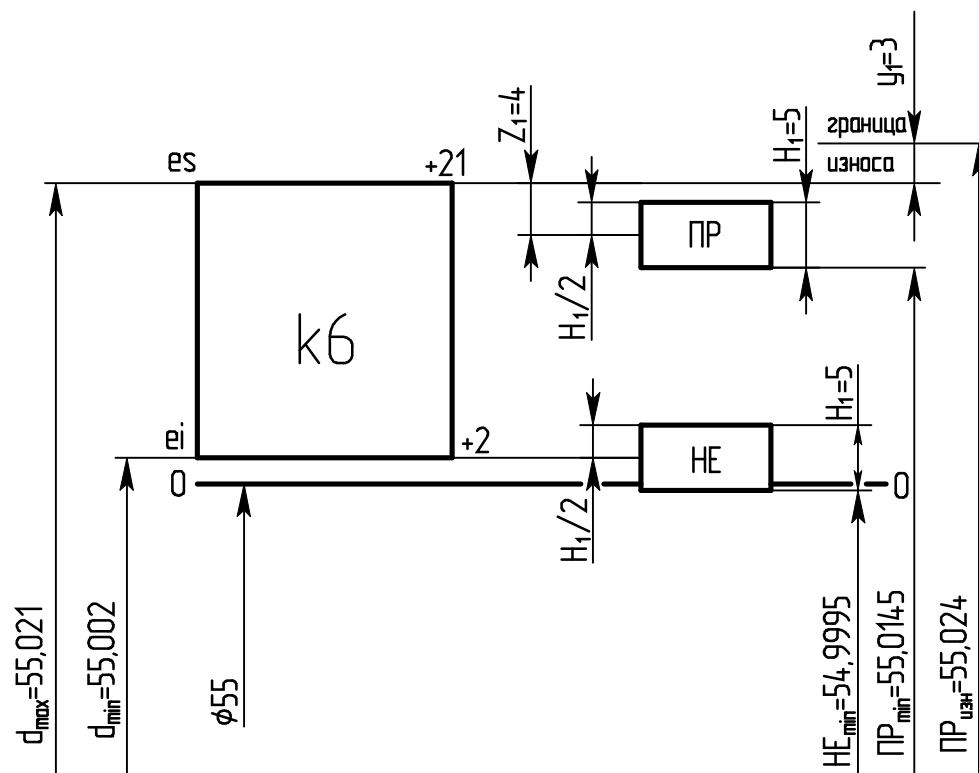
Схема расположения полей допусков калибра-скобы
